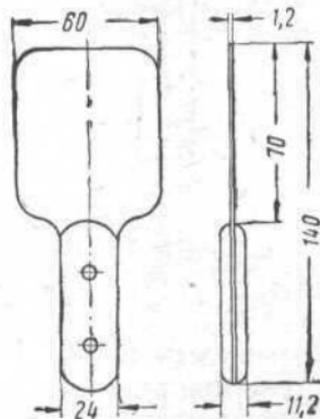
Лопатка для заправки боковой кромки обивки потолка
